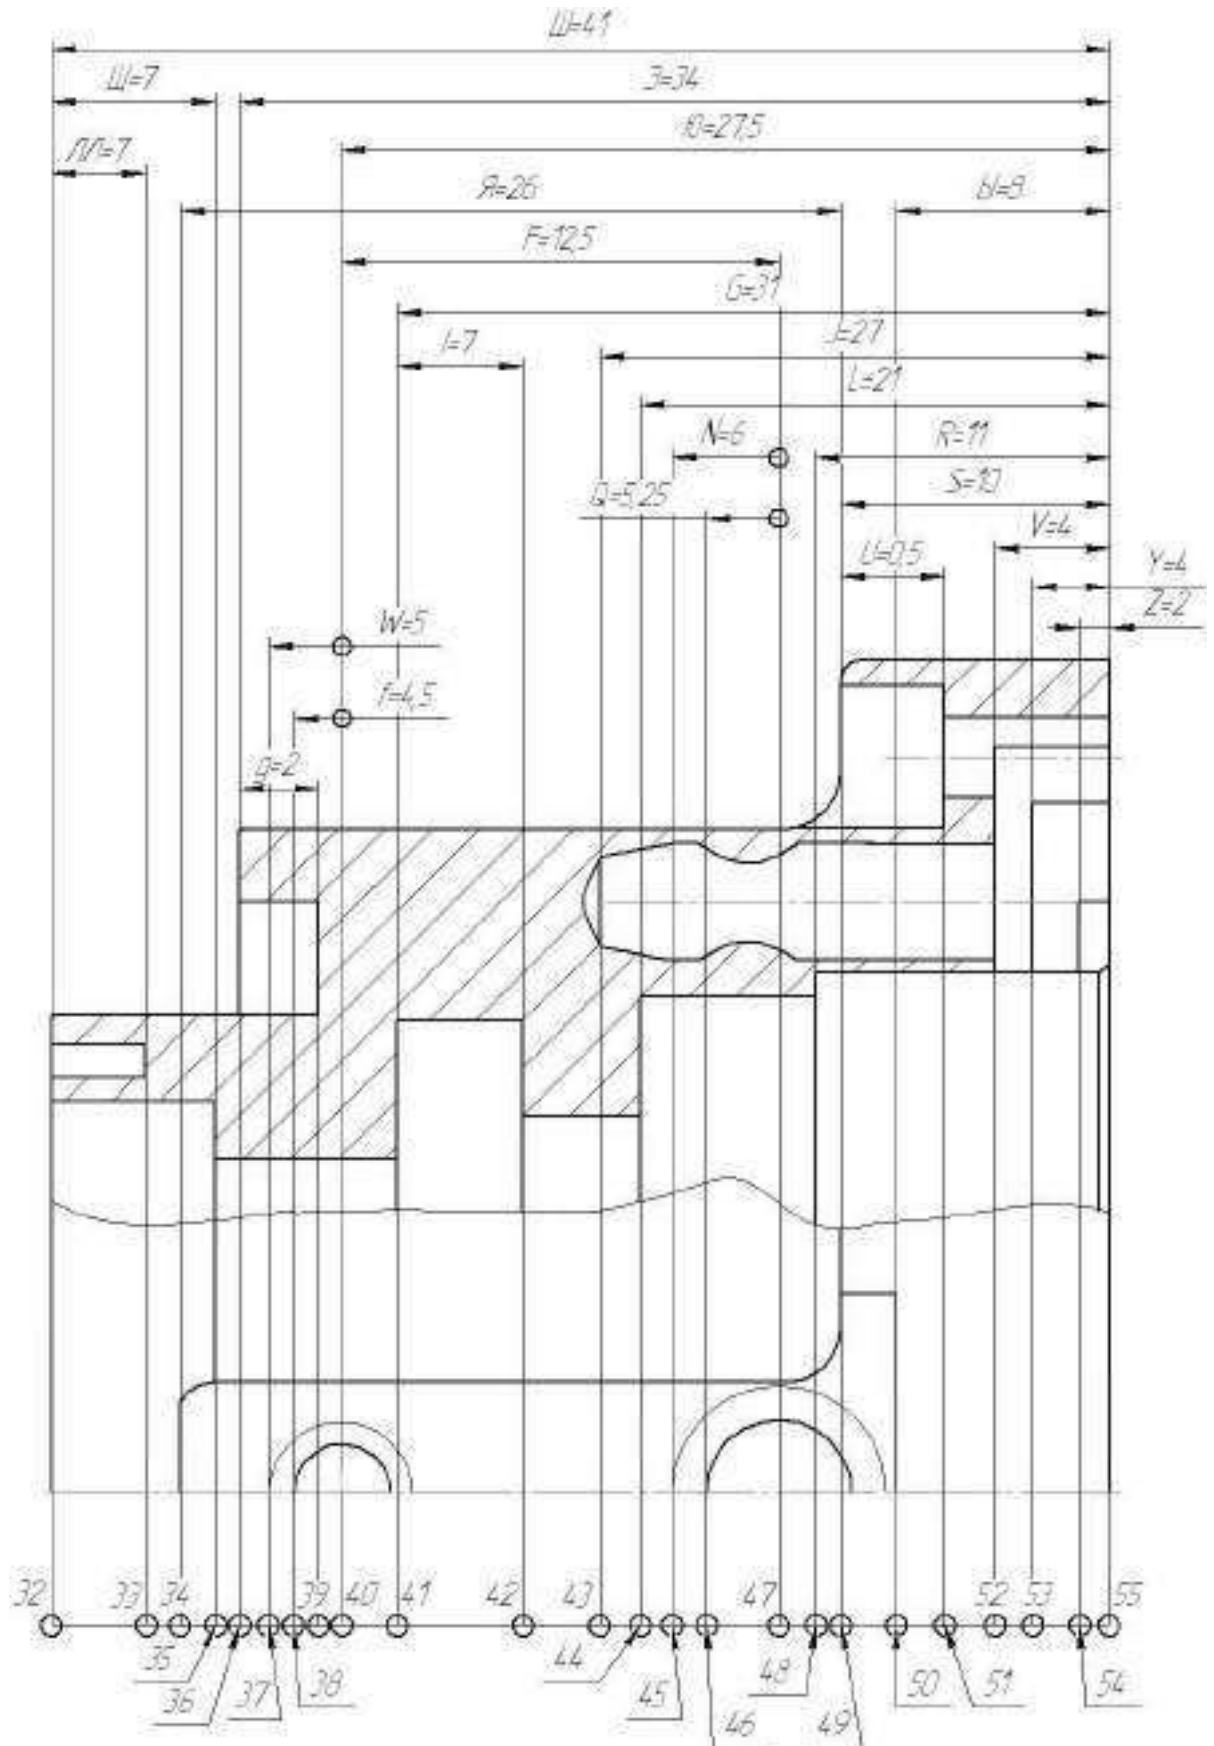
Преобразованный чертёж детали на ось OZ
